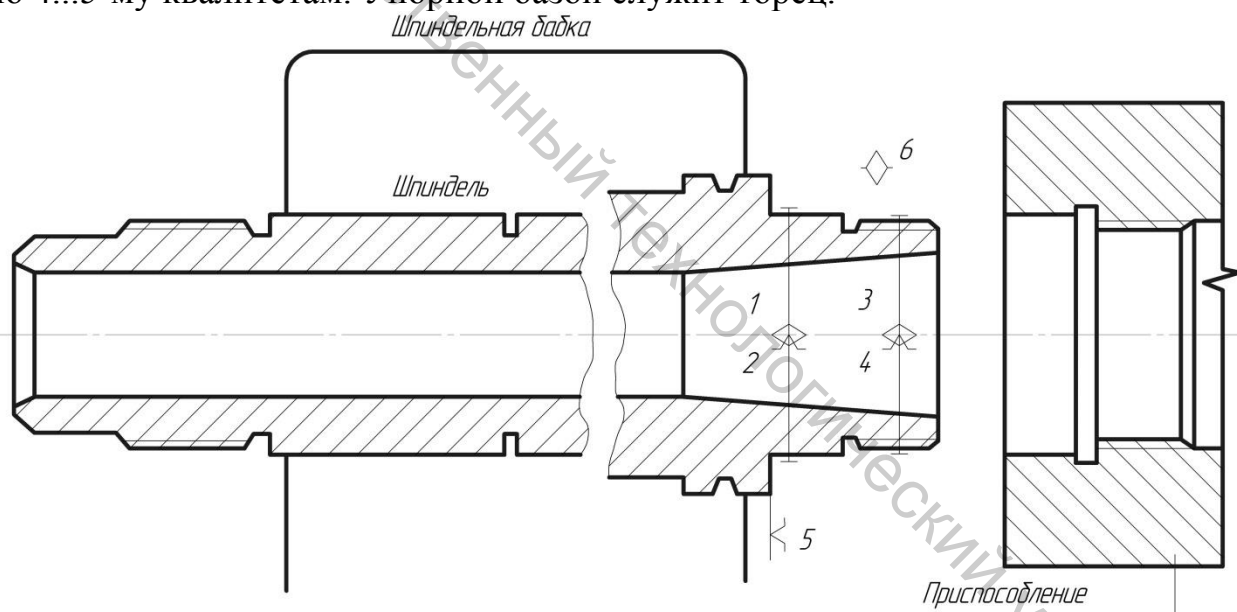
Схема базирования приспособлений на шпинделе токарного станка с резьбовой базой (базовые точки указаны по вспомогательным базам шпинделя)
